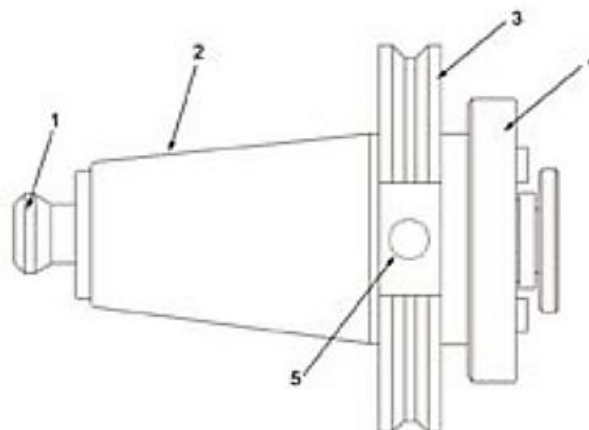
Estrutura principal de um cone de fixação de ferramentas para fresadora (Dormer Tools, 2005)
